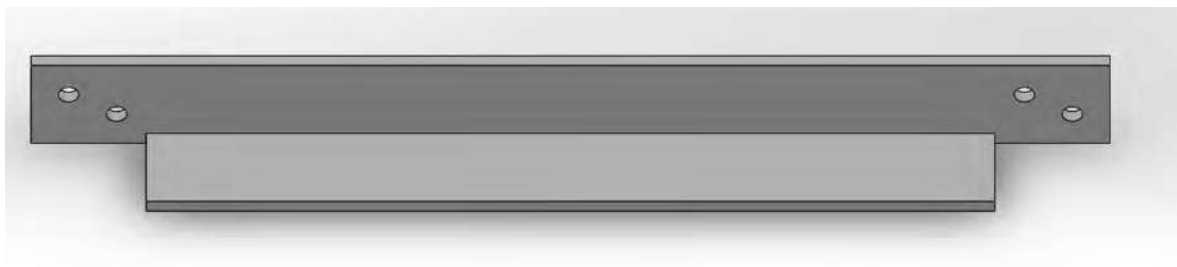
Soporte barra unión de aluminio, con detalle de corte y barrenos.
